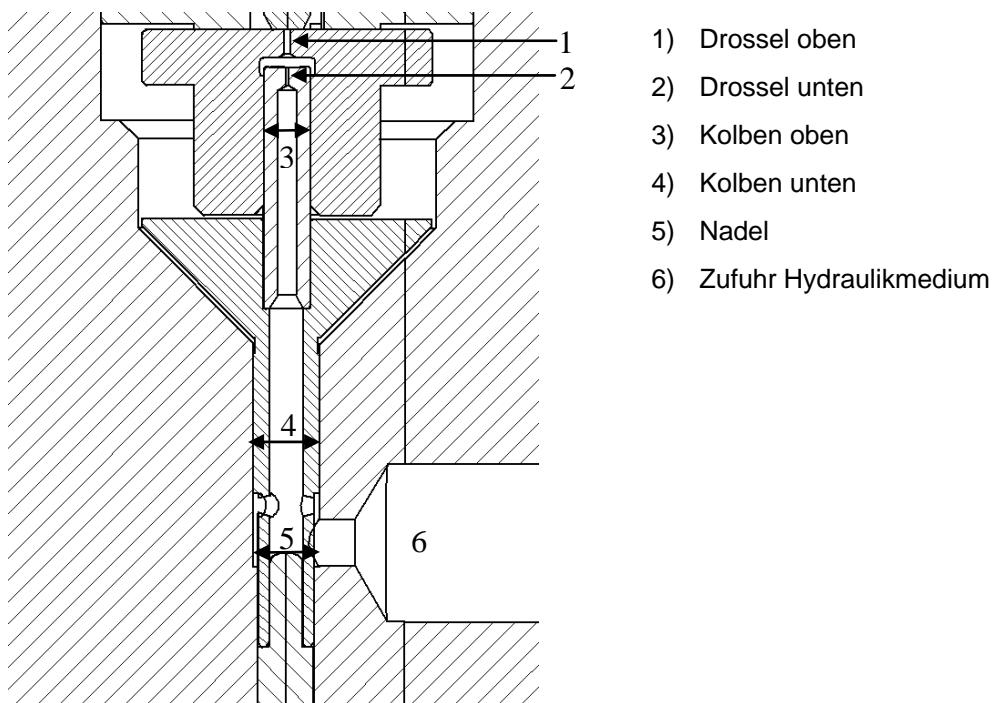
Schema des Hydraulikantriebs mit der Bezeichnung der hydraulisch wirkenden Flächen und Drosseln.
